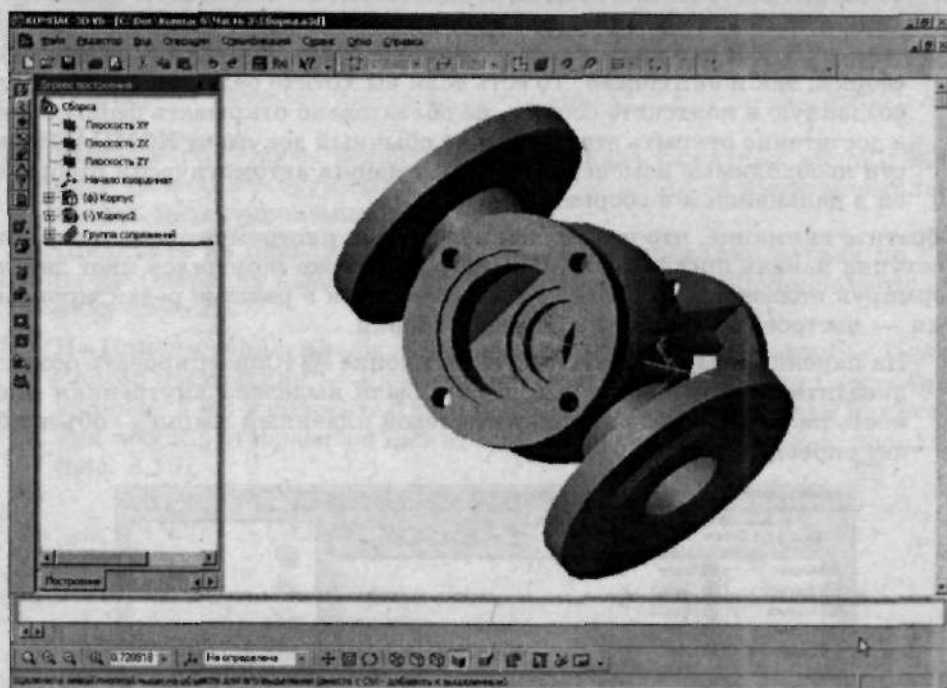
Поверните деталь для того, чтобы создать эскиз будущей детали
